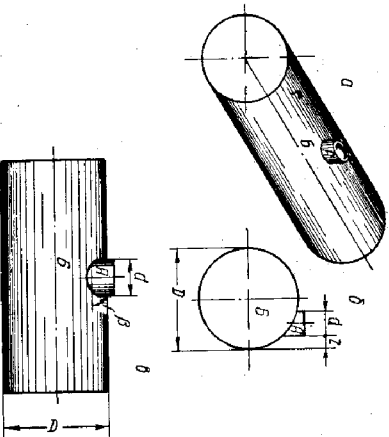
Горизонтальный цилиндрический резервуар.  $a$  — обхват люка;  $b$  — вид с торца;  $e$  — боковой вид.
